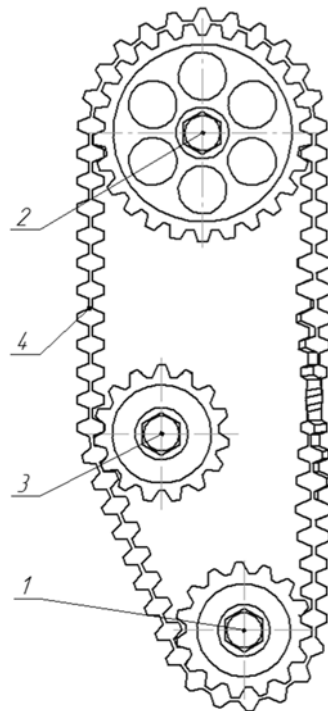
Ремінний привід газорозподільного механізму двигуна:
